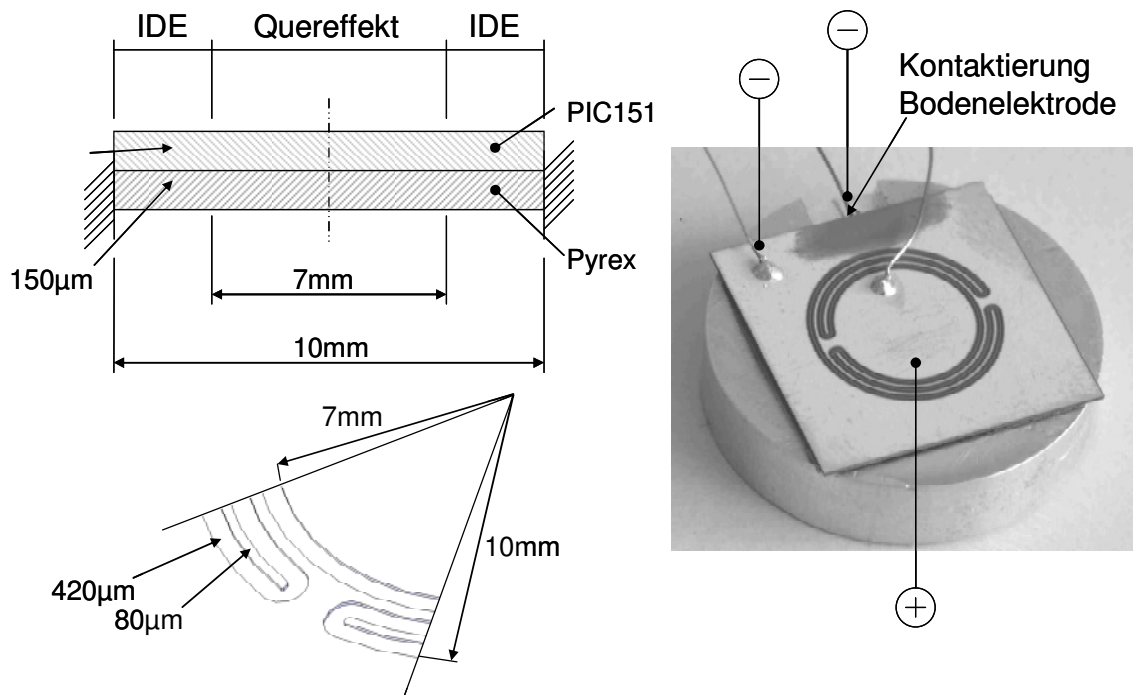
Dimensionen beim Labormuster des kombinierten Wandlers.
